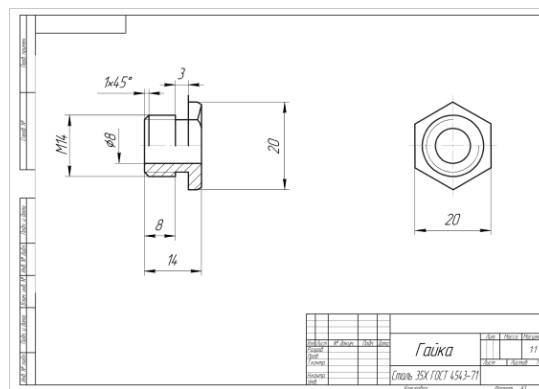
Уточненный рабочий чертеж детали «Гайка»
